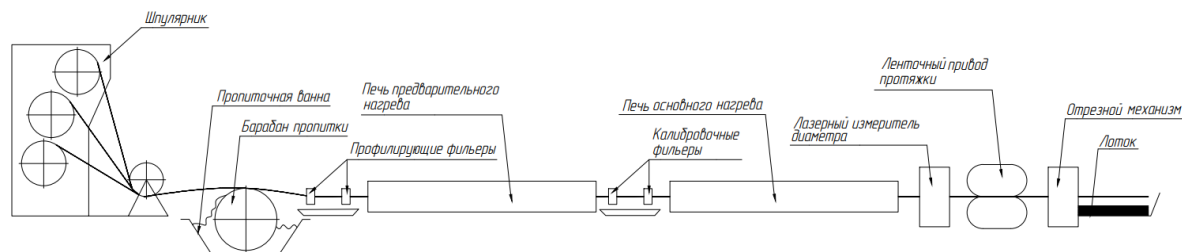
Схема пултрузионной установки для изготовления стержней из углеродного волокна
